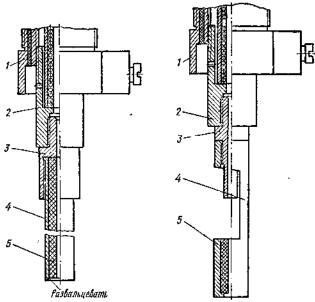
Схема опытной приставки к держателю для сварки с увеличенным вылегом электрода:
